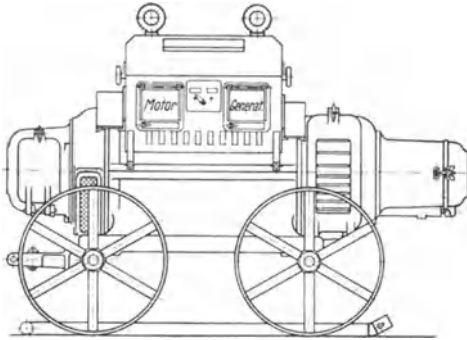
Fahrbarer Gleichstromschweißumformer.
